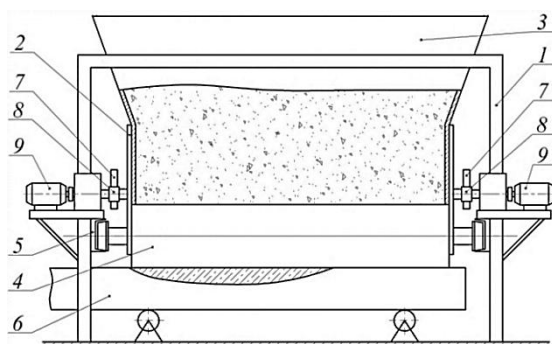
Роликова формувальна установка з кулачковим приводним механізмом
